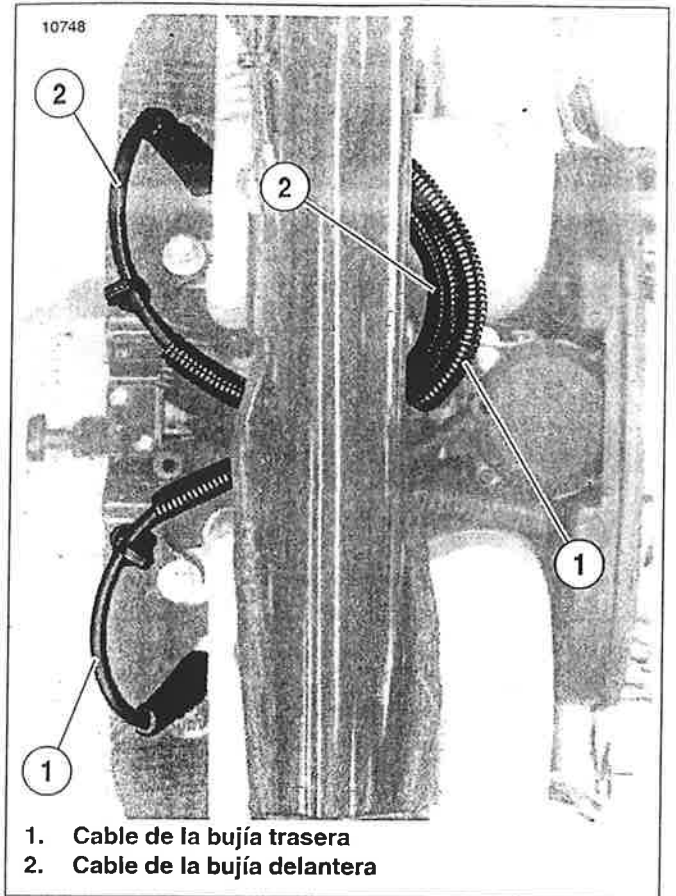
Presilla de cable abierta en la pieza de soporte de la culata del cilindro
